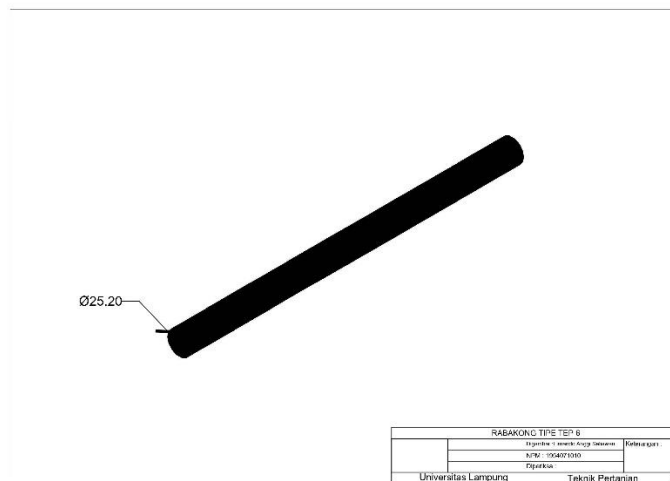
Mata pisau *chansaw steel* tampak 3d
